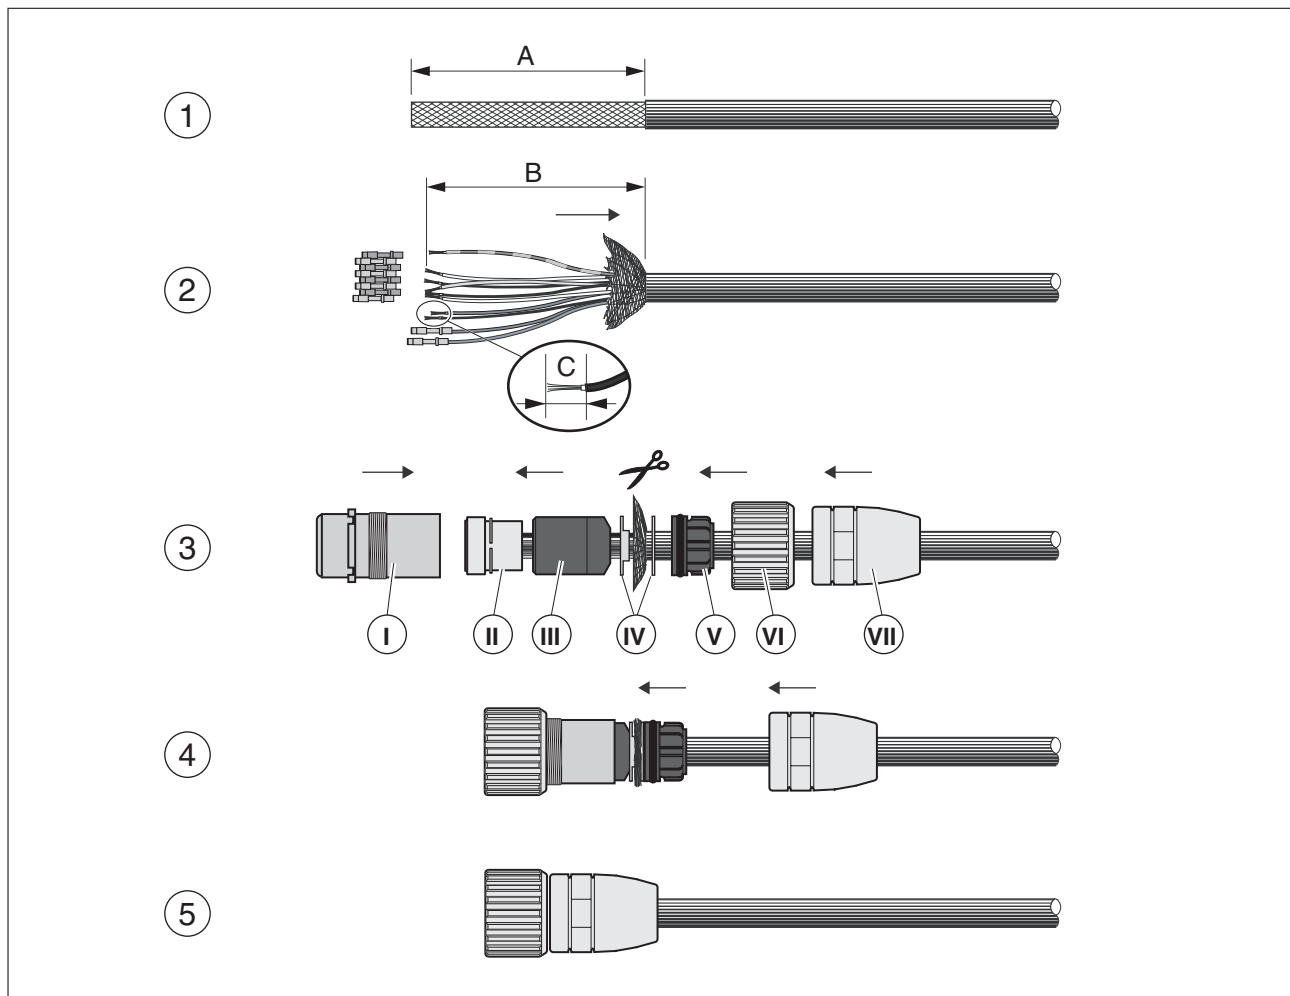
Assemblare il cavo encoder con il connettore encoder M23
